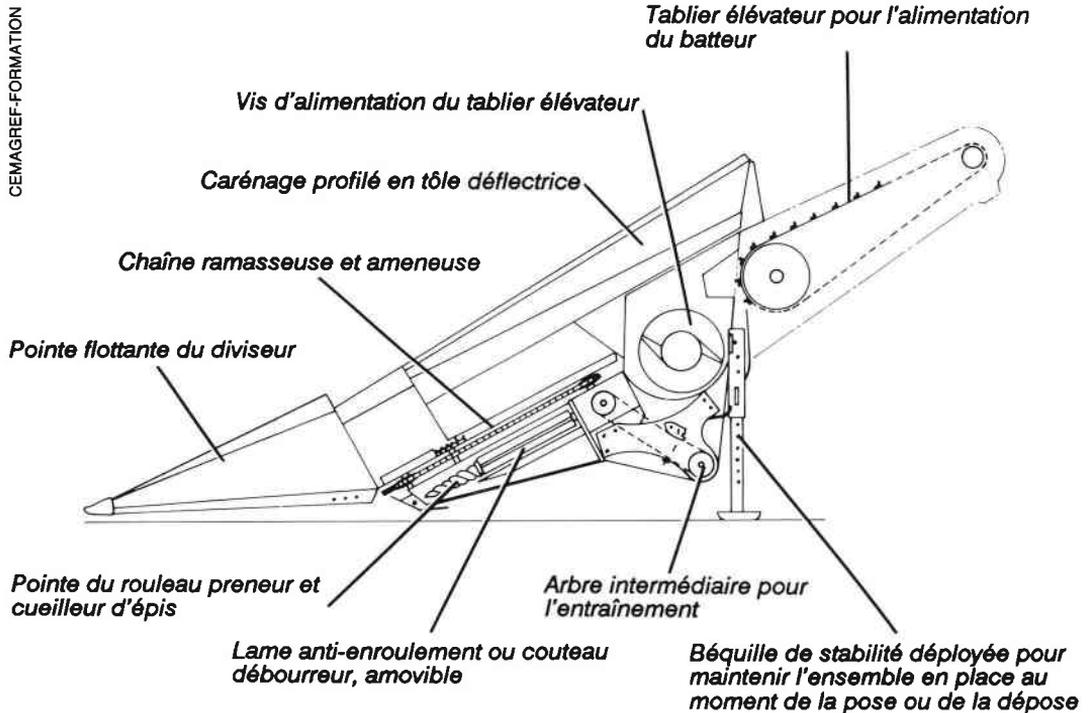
Vue en coupe d'un bec-cueilleur de maïs.
